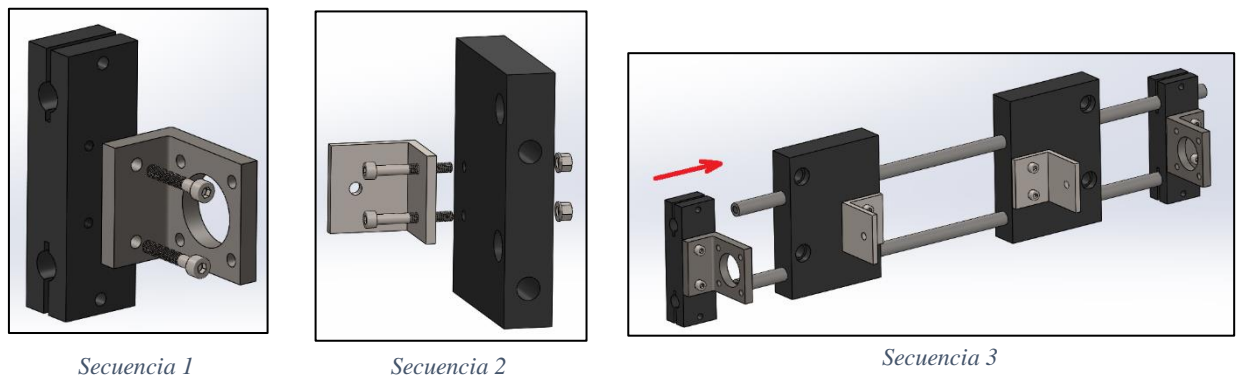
Montaje grupo de piezas de guiado (SS)
